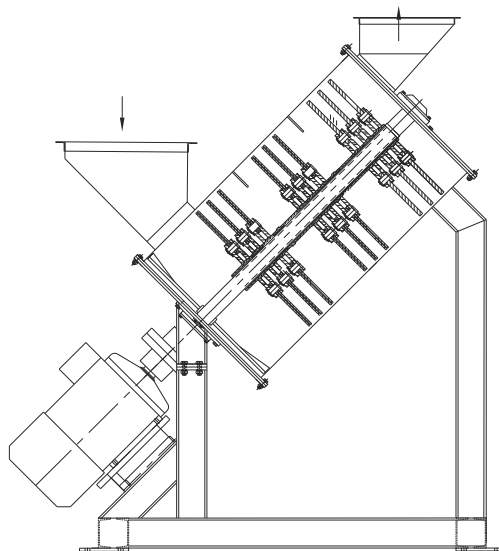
Молотковая дробилка с нижней загрузкой обрабатываемого материала
